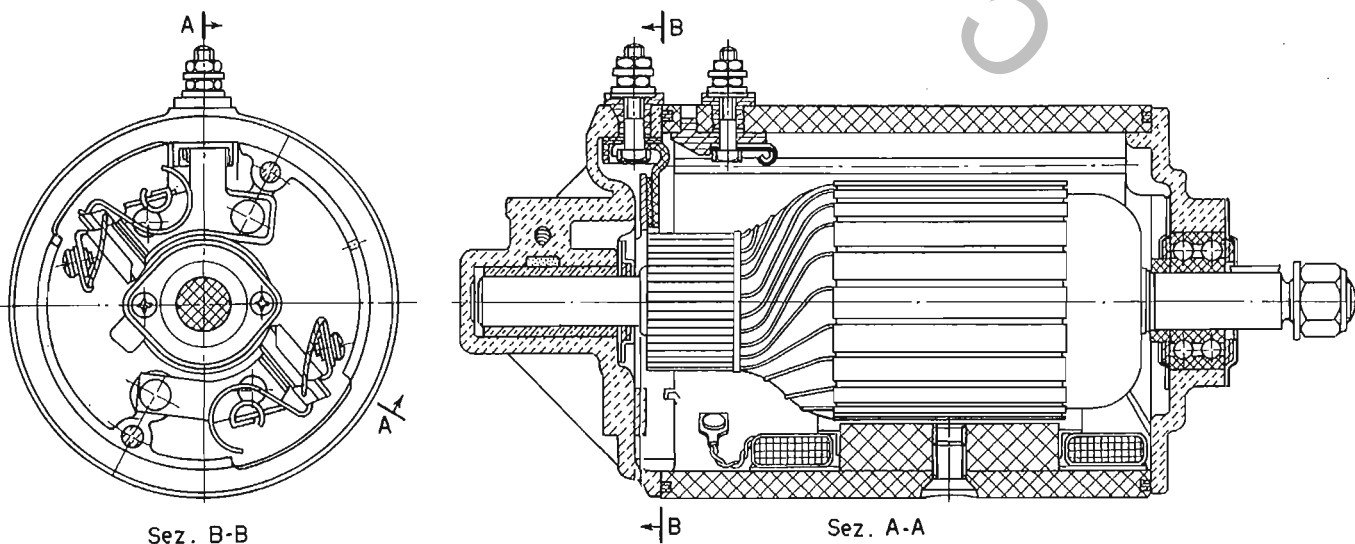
Sezione longitudinale e trasversale della dinamo tipo DC 115/24/7/3 C.
